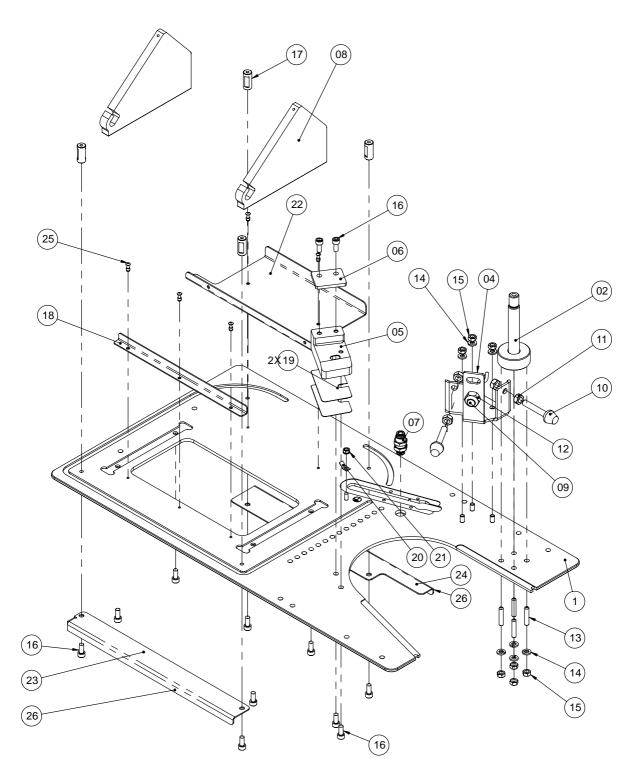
Ersatzteile Baugruppe Trägerplatte oben
